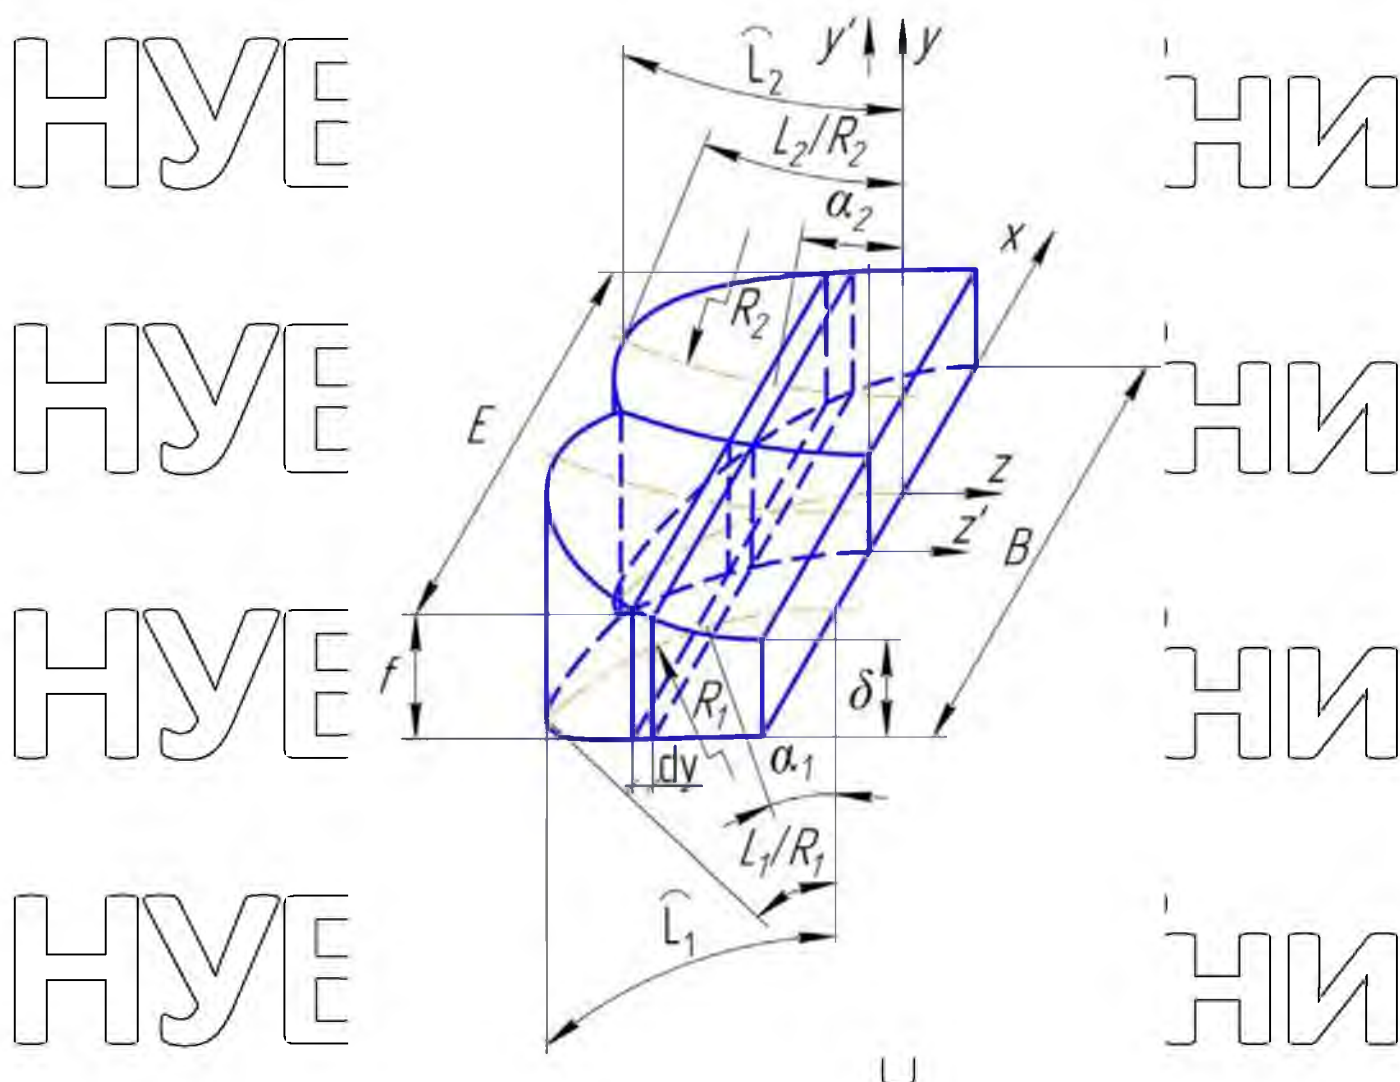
Єдина ділянка металопокриття при формуванні зведеного зварного шва
